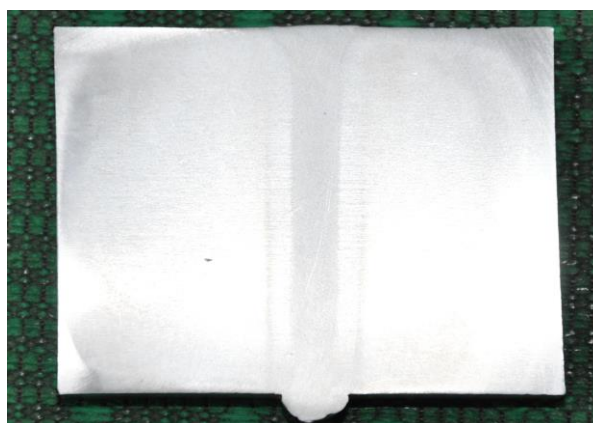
Макрошлиф сварного соединения ЭЛС $t=90$ мм.
